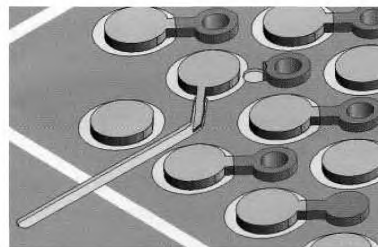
б – Удаление площадки BGA и фрезерование канавки в поверхности паяльной маски
